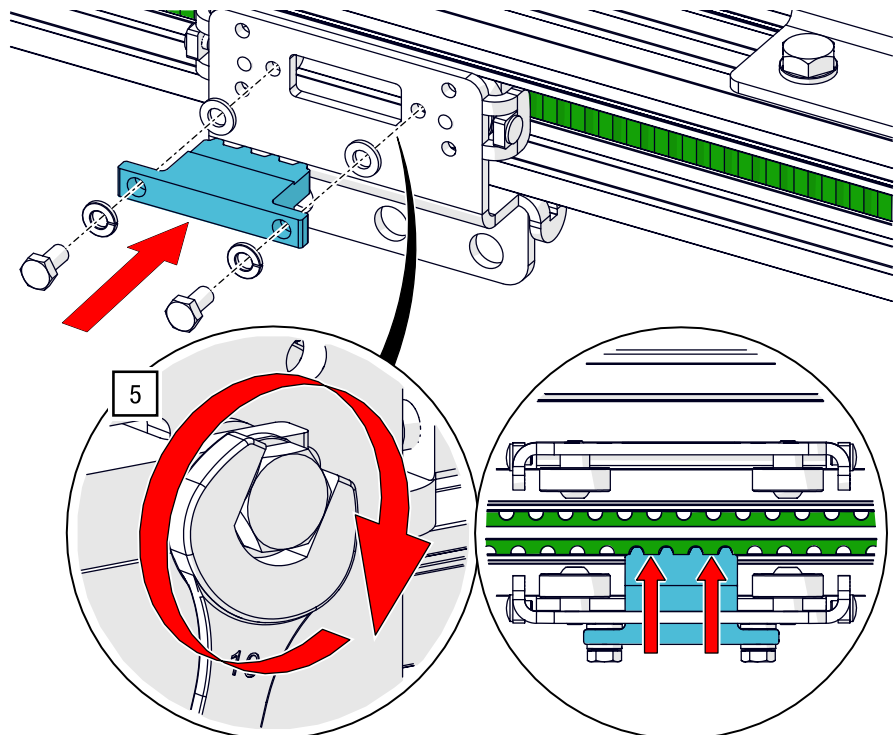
Zahnriemenmontage – Zugwagen mit dem Riemenkamm befestigen
